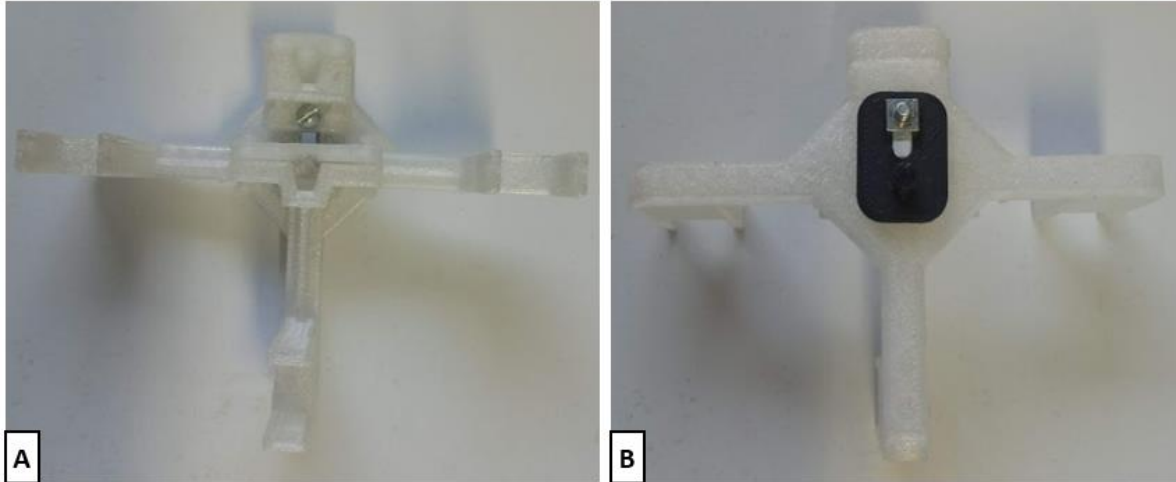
Soporte en "T" V4, fabricado en PLA, (A) Vista frontal; (B) Vista posterior
